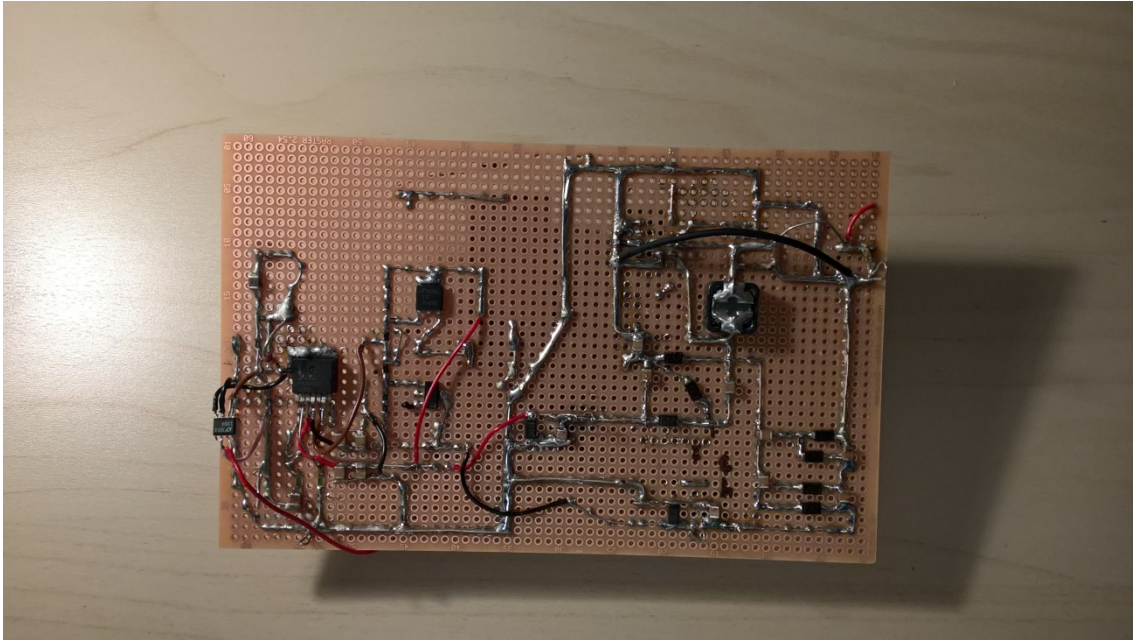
Vista de la parte soldable de la placa de prototipado.
